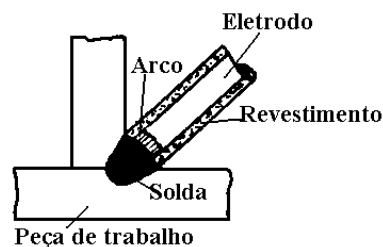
Soldagem por eletrodo a curto-circuito utilizado na solda de ângulo.
